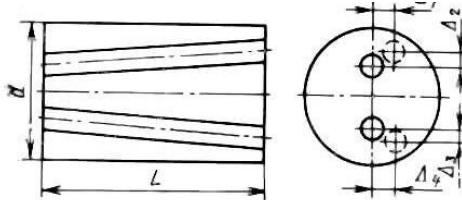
Отклонения расположения обрабатываемых поверхностей отверстий
